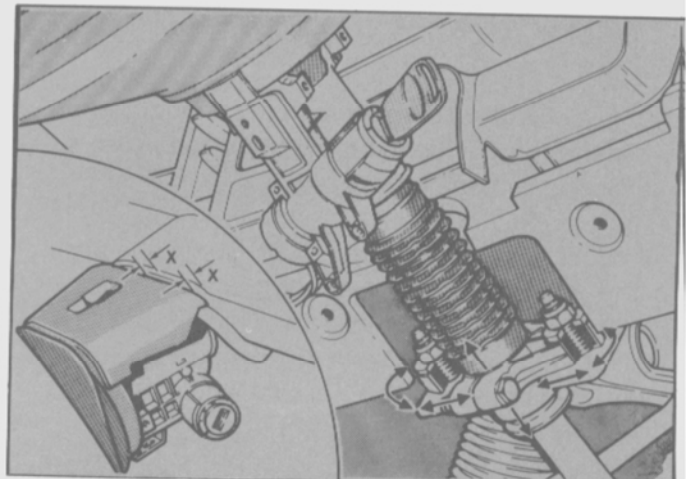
Distancia entre cubierta superior y panel de tablero.
